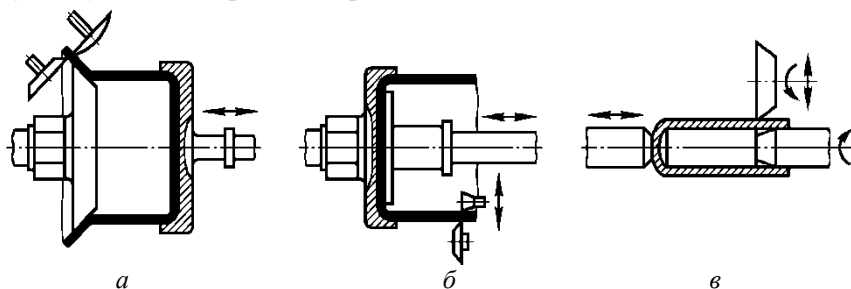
Обрезка дисковыми ножами заготовок с фланцем (*а*), без фланца (*б*) и в патронном производстве (*в*)
